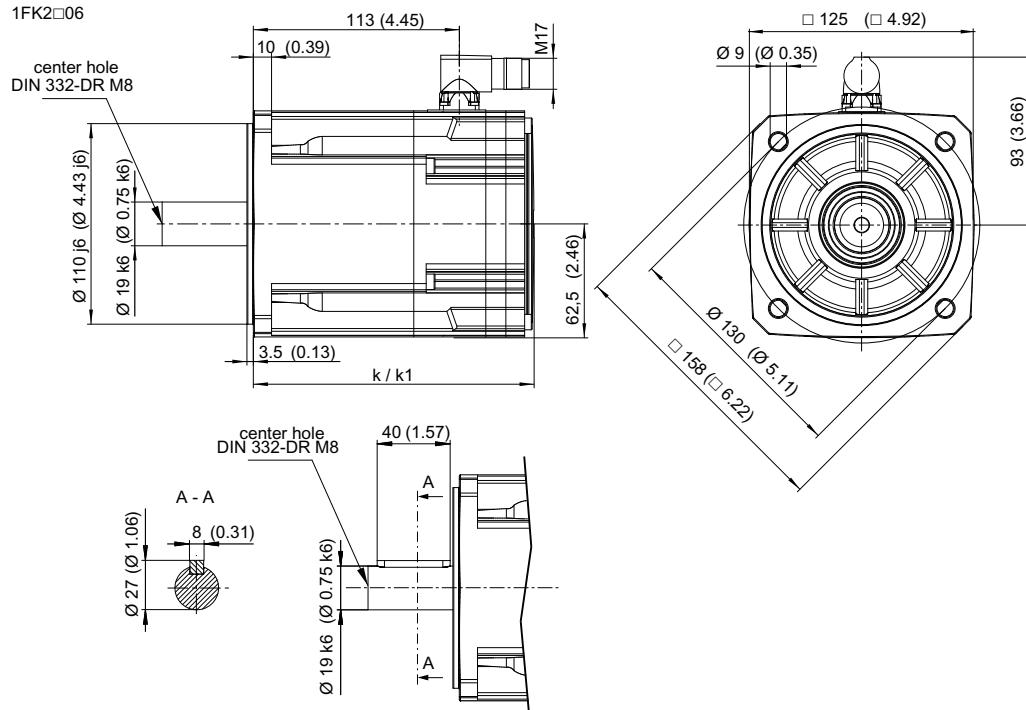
Maßzeichnung_1FK2206-2AF00-0SA0
